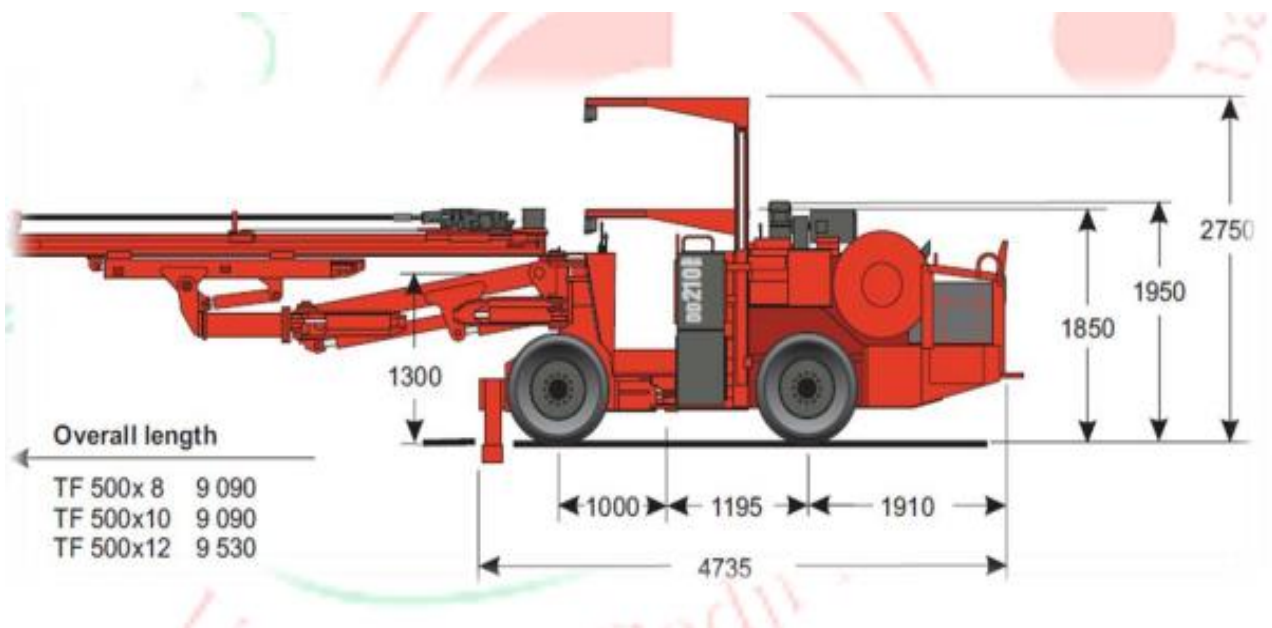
les différentes dimensions de la machine Sandvik DD210 en mm
